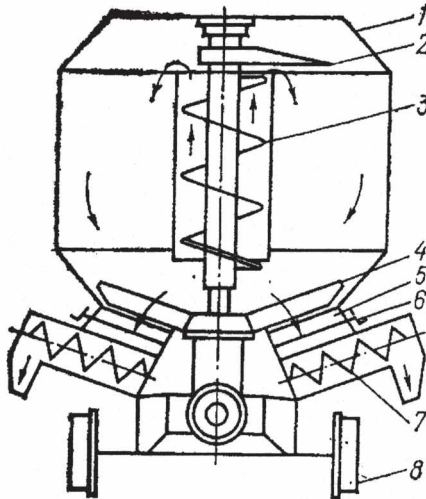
Конструктивно-технологічна схема роздавача КС-1.5: 1 - бункер; 2 - розрівнювач; 3 - вертикальний шнек; 4 - лопатева мішалка; 5 - камера; 6 - засувка; 7 - вивантажувальний шнек; 8 - ходова частина.
